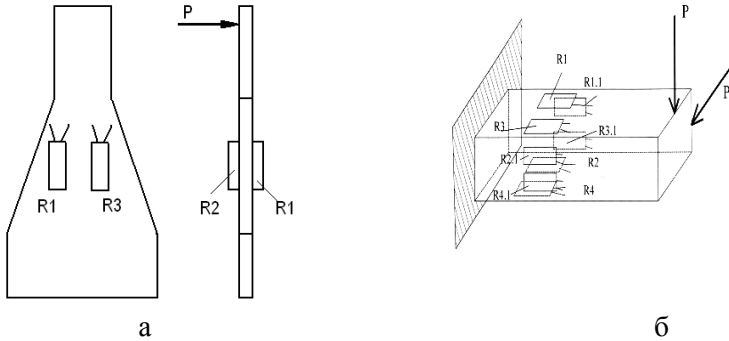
Схема расположения тензорезисторов на балке равного сопротивления (а) и державке резца (б)
